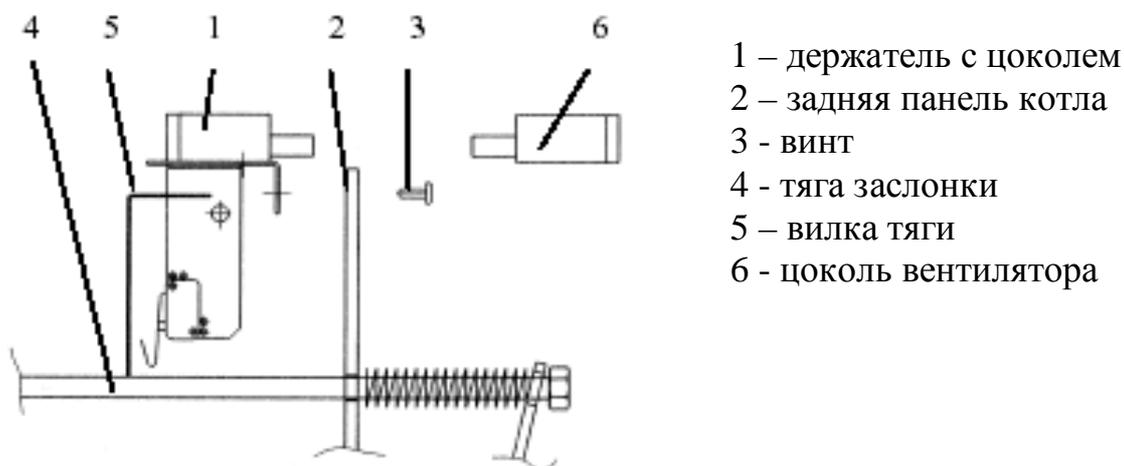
Монтаж семиполюсного цоколя с держателем.
